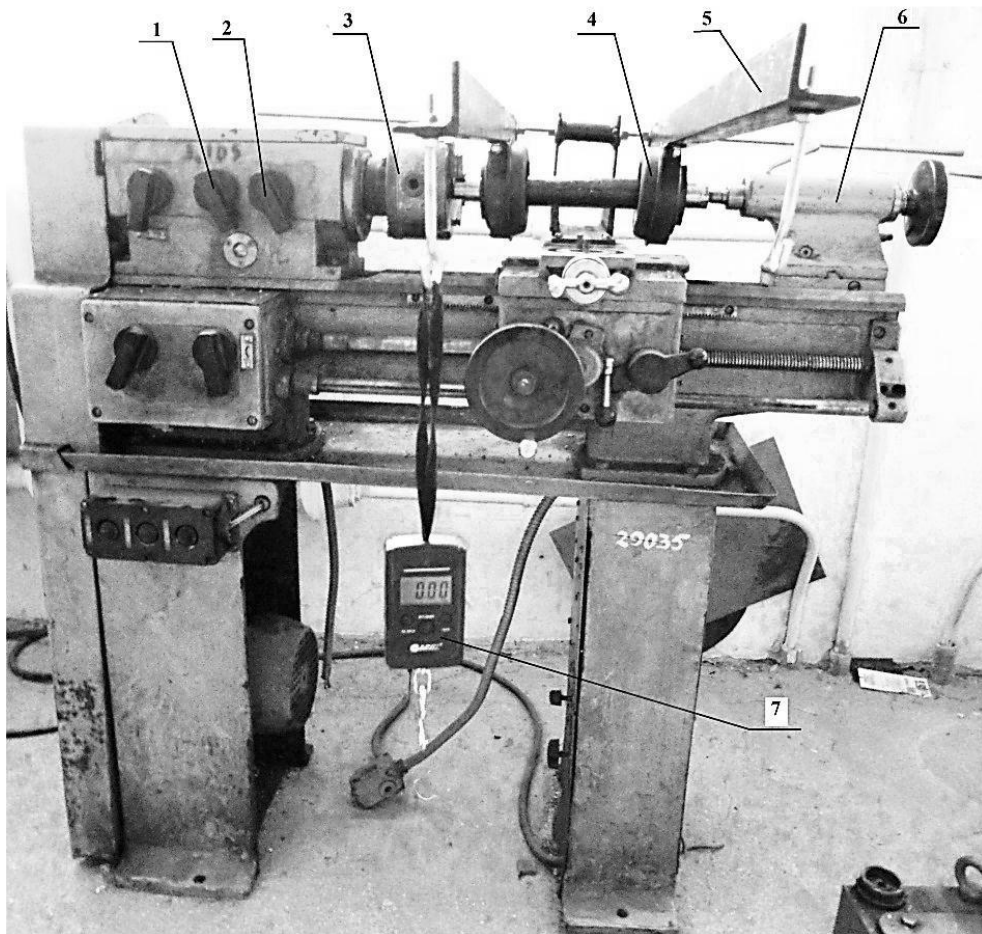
Випробувальний стенд на базі токарно-гвинторізного верстата ТВ-6: 1,2 – рукоятки установки частоти обертання шпинделя, 3 – шпиндель верстата, 4 – підшипникова опора, 5 – навантажувальний важіль, 6 – задня бабка верстата, 7 – динамометр.
